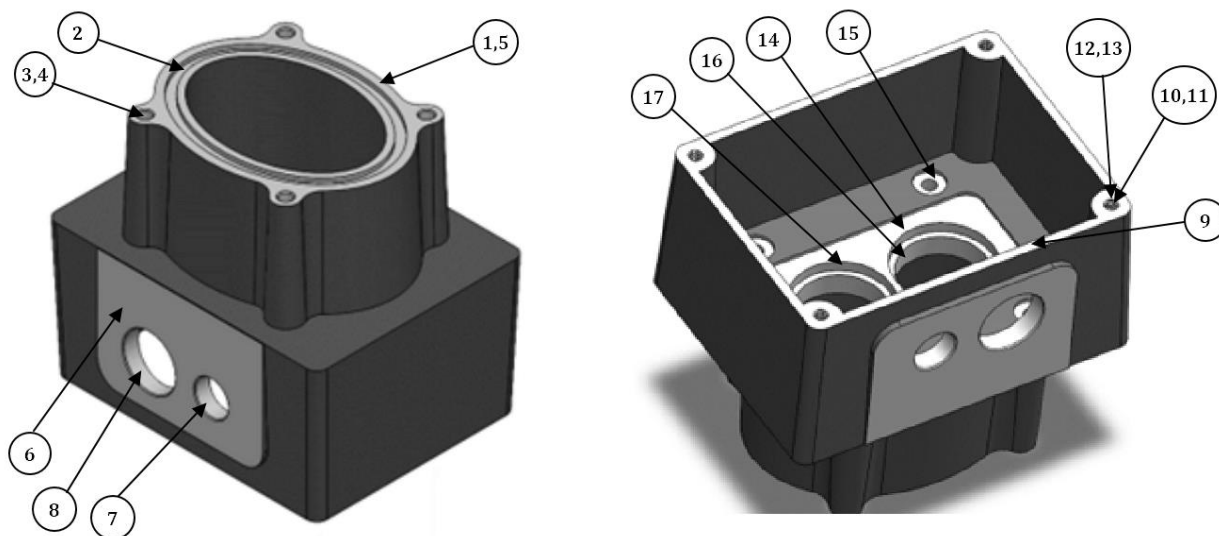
Деталь «Клемна коробка» та номери поверхонь, що обробляються
